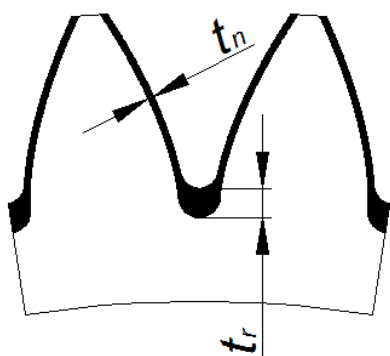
Припуск под получистовое зубофрезерование в первой позиции обката
